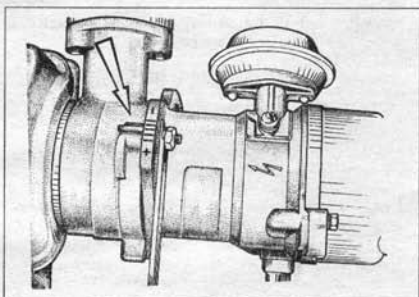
Установка датчика-распределителя зажигания. Стрелкой показан установочный выступ на корпусе вспомогательных агрегатов
